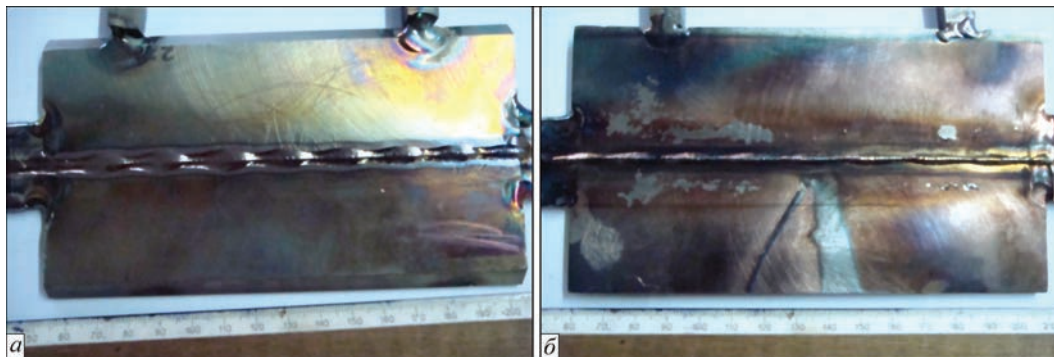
Общий вид сварного соединения сложнолегированного высокопрочного титанового сплава, полученного ЭЛС: *a* — лицевая, *b* — корневая сторона
